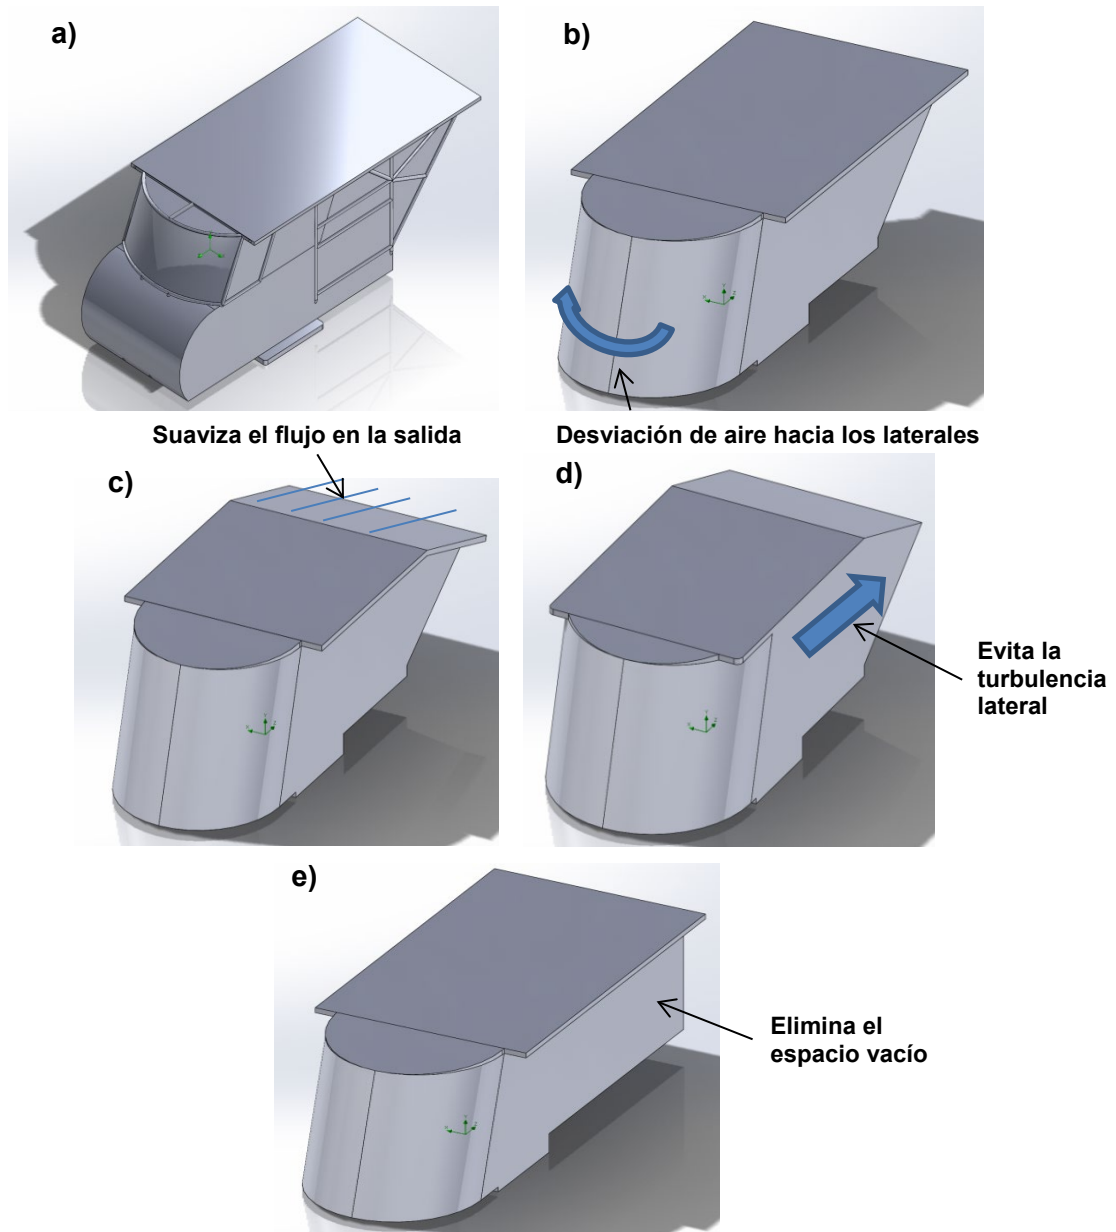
Diseños de carrocería: a) Diseño preliminar b) Diseño 1 c) Diseño 2 d) Diseño 3 e) Diseño 4.
